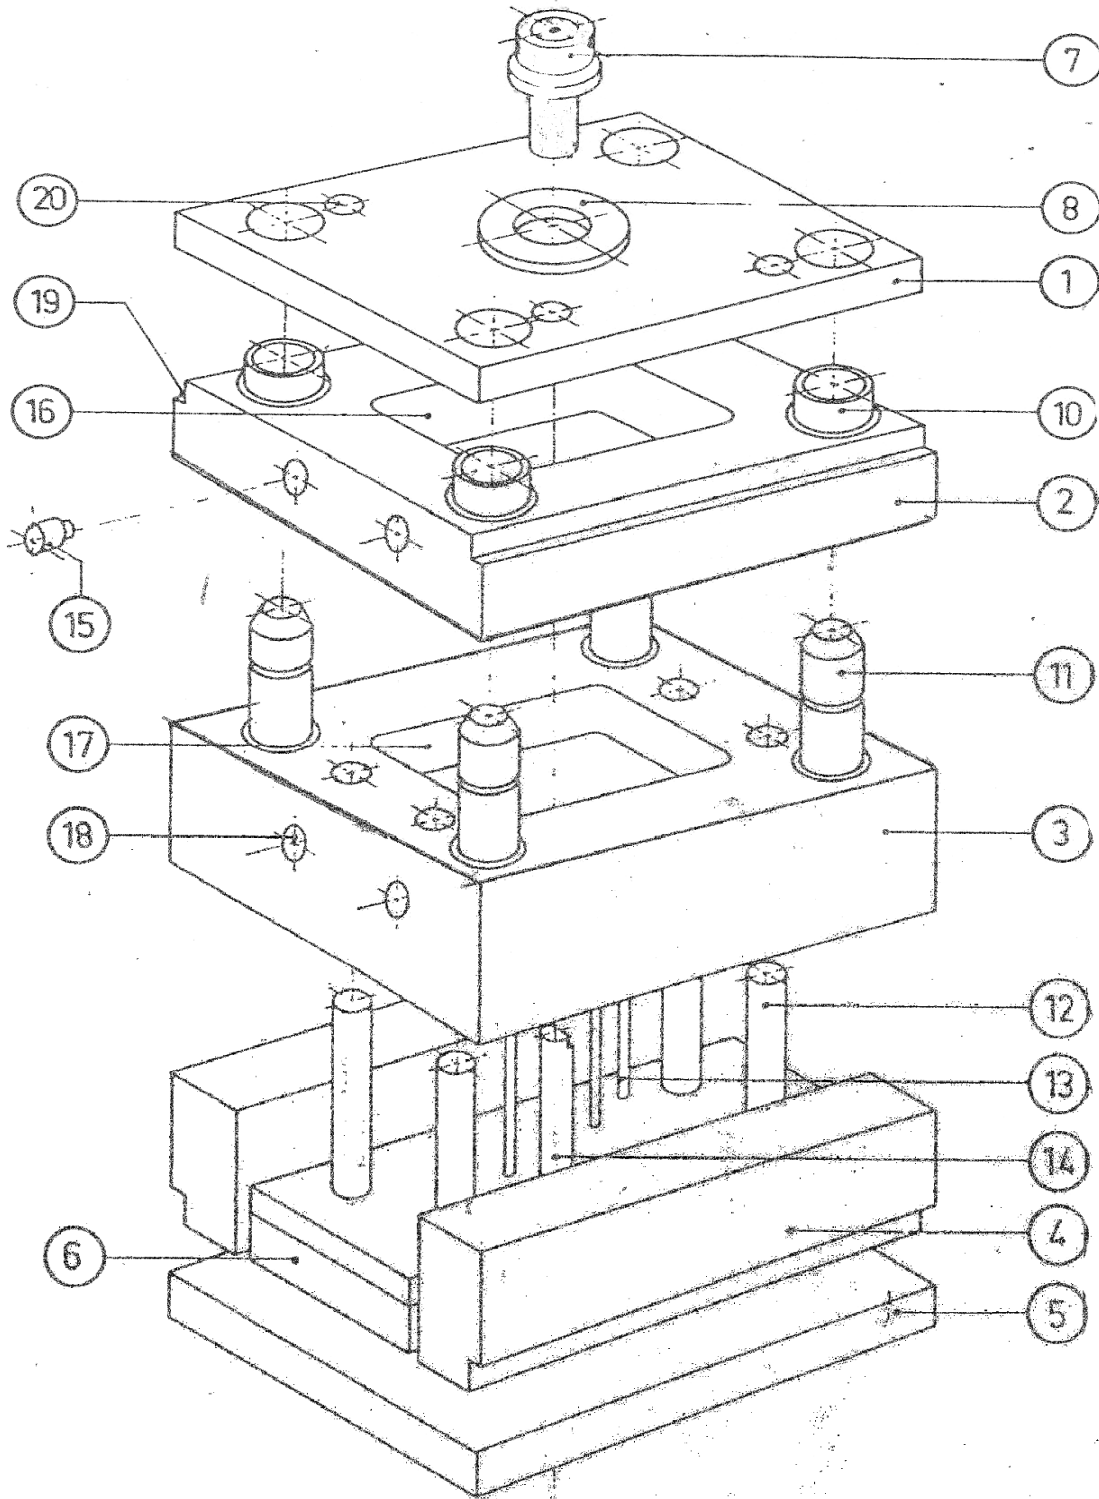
Vue éclatée d'un moule d'injection plastique.
